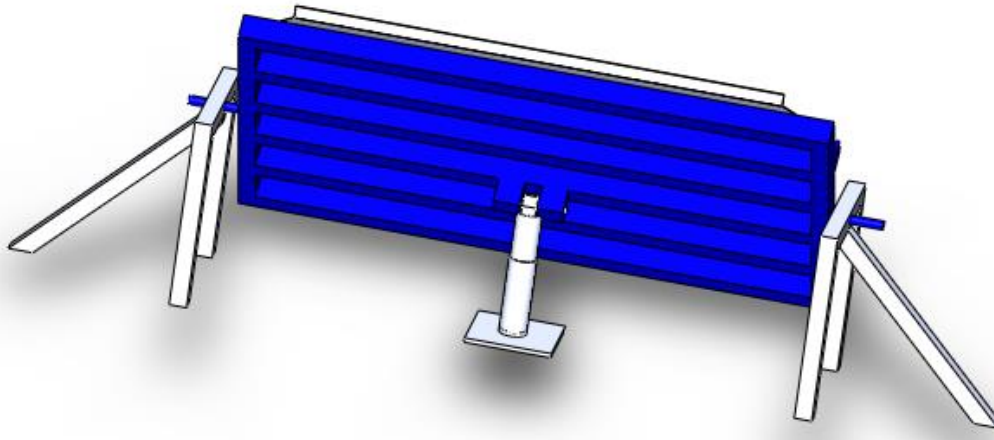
Matriz de soldadura para conjunto frente intermedio y superior.
